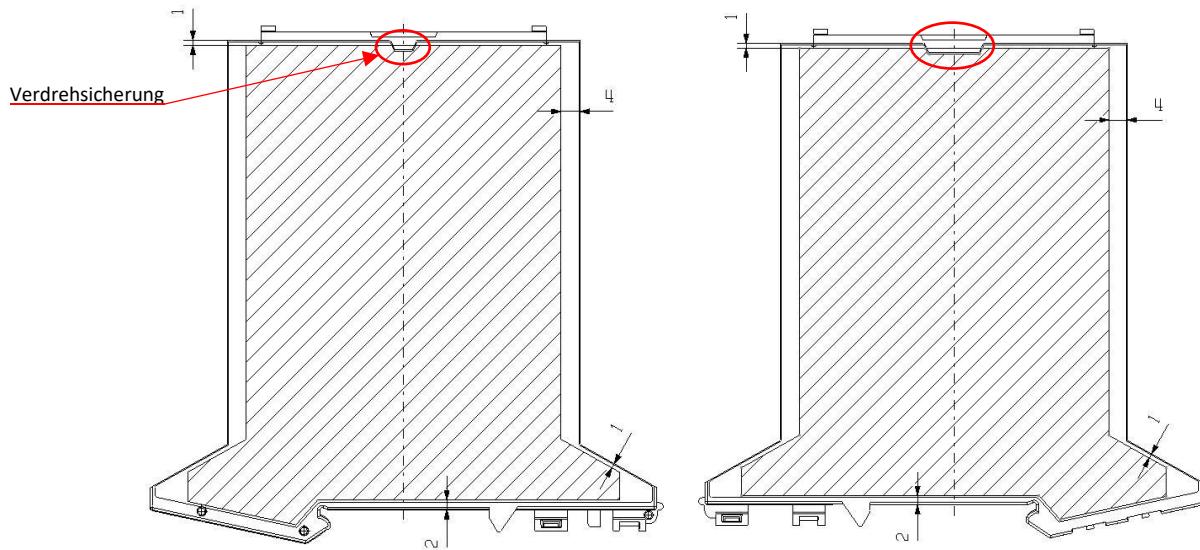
(Base (B) / Seitenansicht li/re / Bearbeitungsflächen
